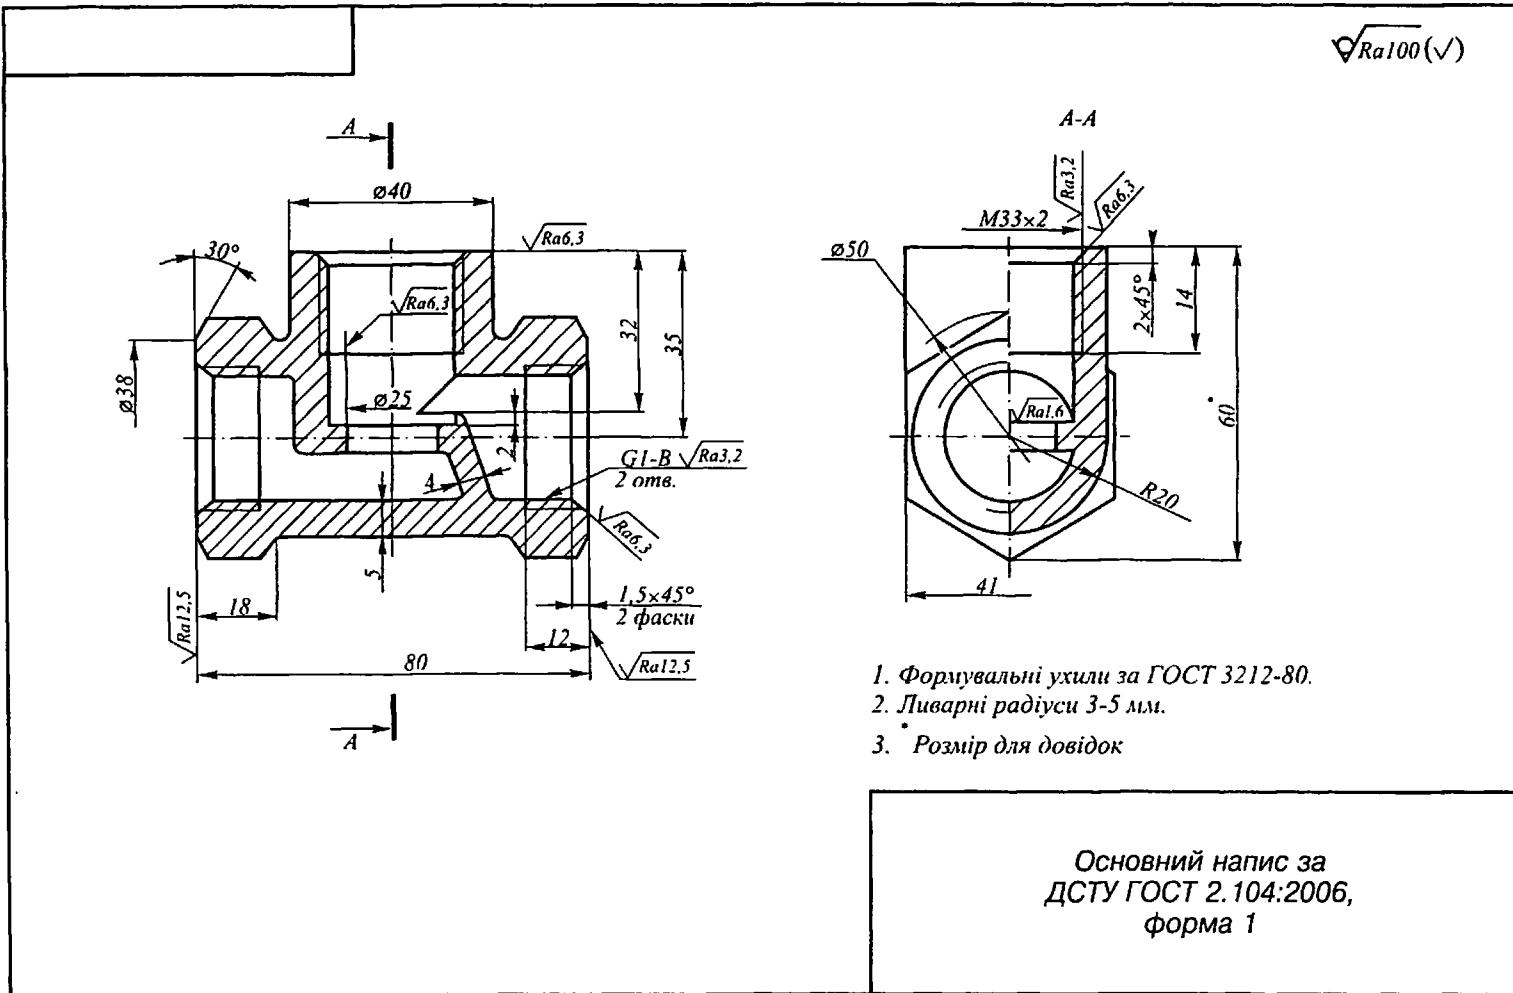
Приклад оформлення кресленника корпусної деталі, виготовленої з литої заготовки
